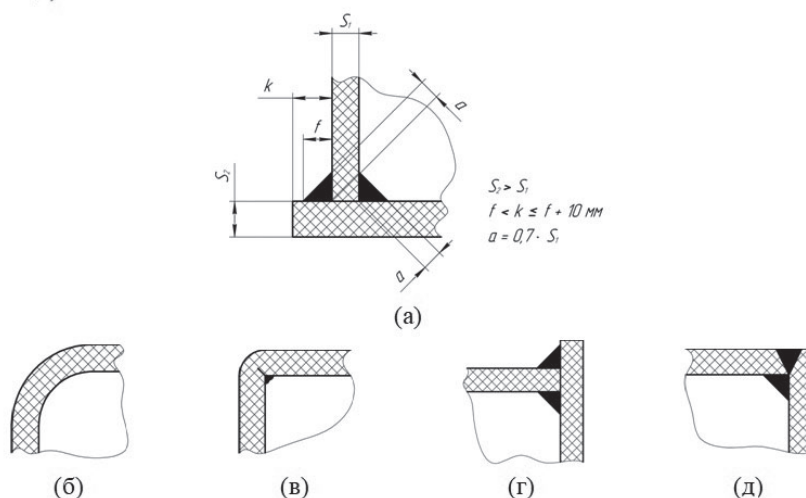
Схема сварного соединения «дно-стенка»: а. – тавровое; схемы угловых соединений «стенка-стенка»: б. – соединение скруглением; в. – соединение гибкой; г. – тавровое сварное соединение; д. – угловое сварное соединение
